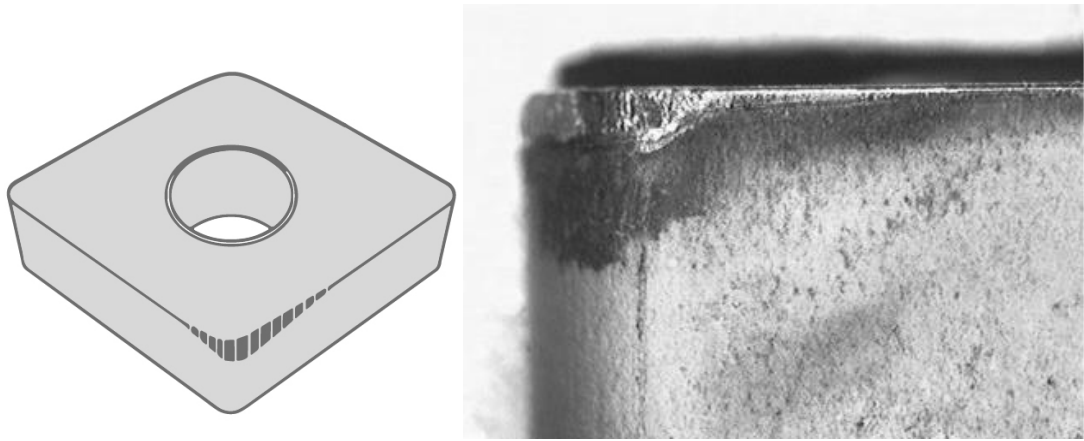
Зношення швидкоріжучої пластини по задній поверхні
